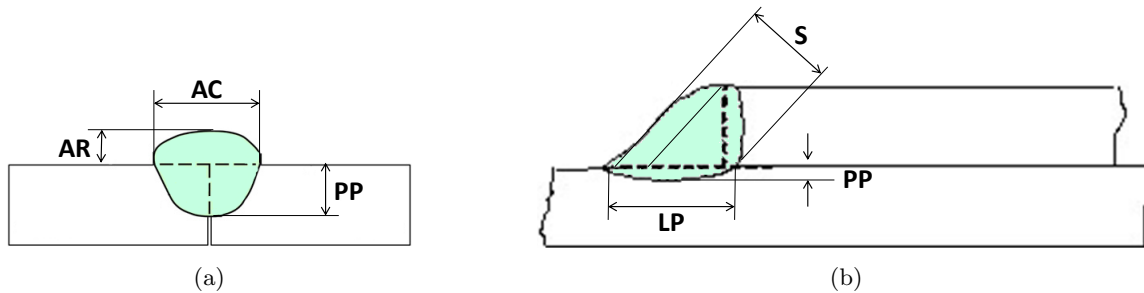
(a) Soldadura a tope y (b) soldadura a solape, con sus principales dimensiones [11,12].
